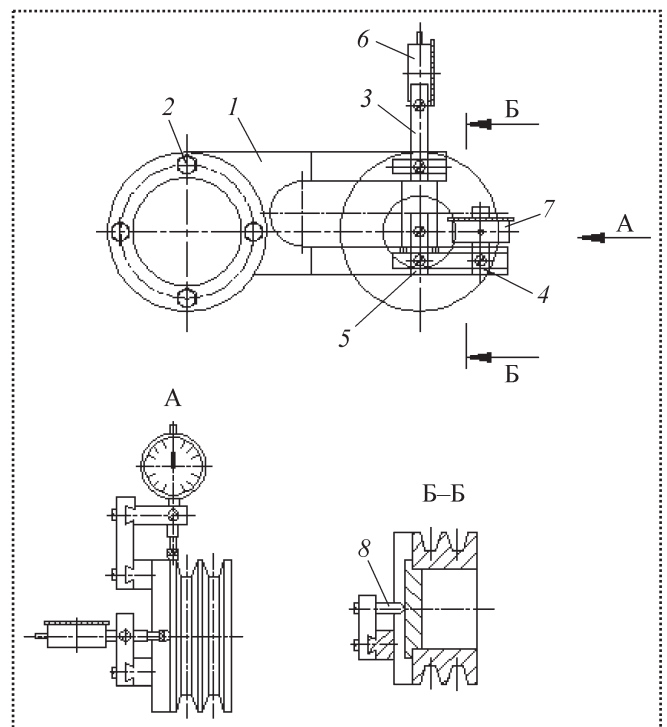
Контрольно-измерительное приспособление для клиноременных передач
